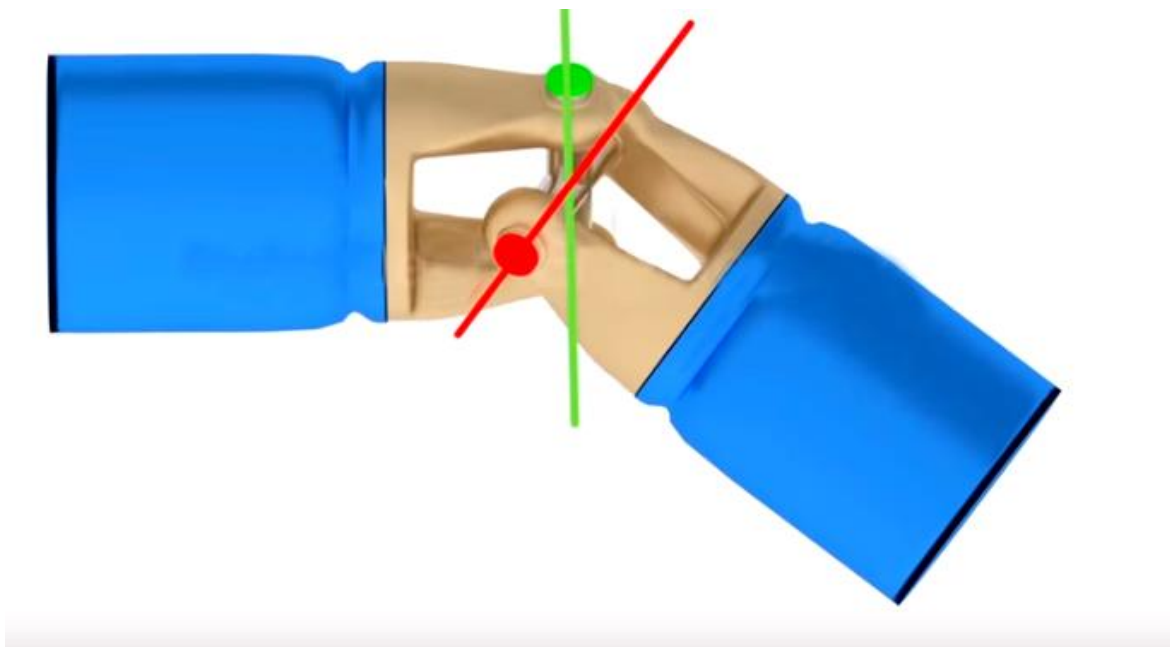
Универсальный шарнир модель – схема – движение под углом.
